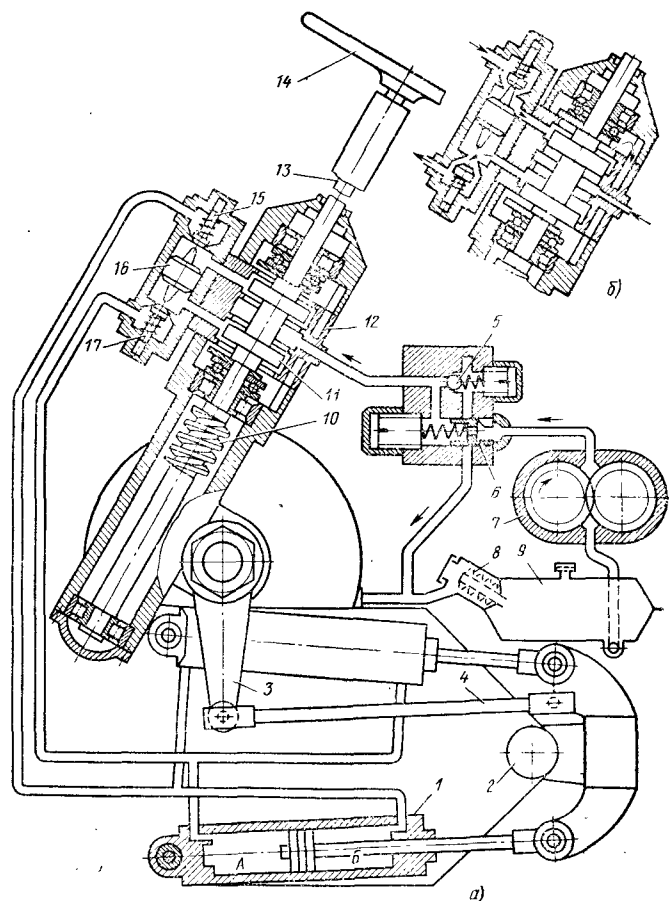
Схема рулевого управления трактора с шарнирной рамой для положения золотника распределителя и запорных клапанов: а — при прямолинейном движении; б — при повороте вправо
